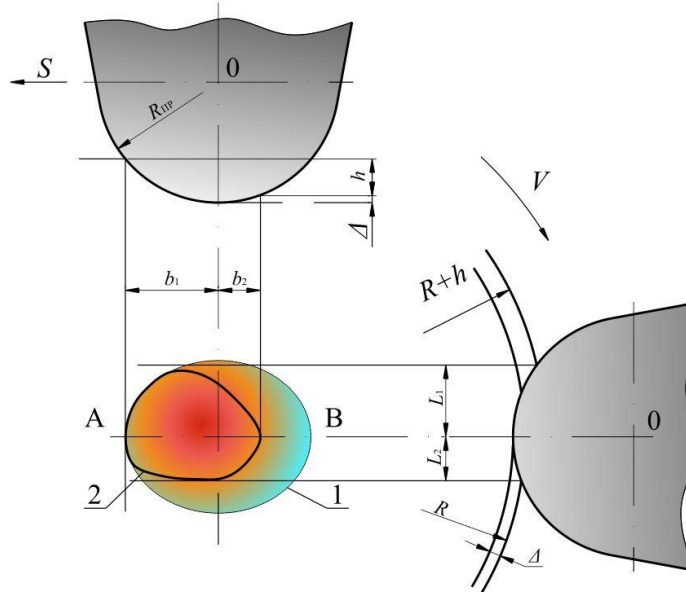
Форма поверхні контакту в процесі вигладжувального оброблення циліндричної деталі індентором із сферичною робочою частиною
